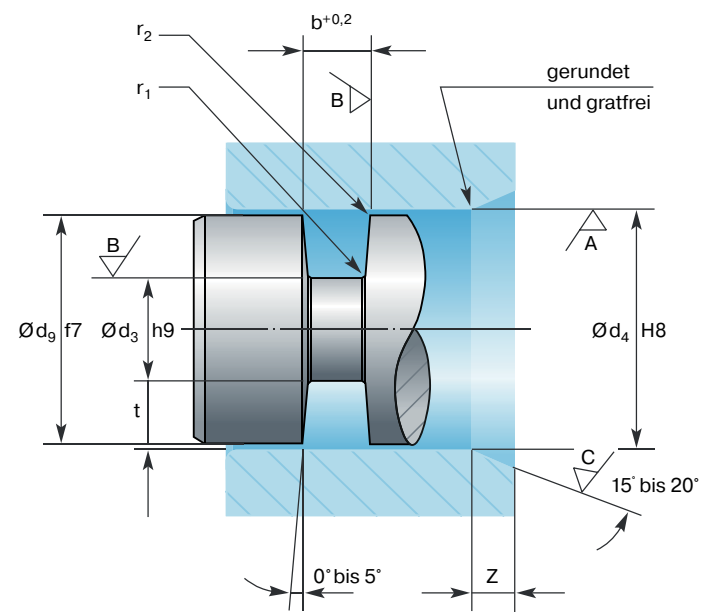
Kolbendichtung – Hydraulik und Pneumatik
